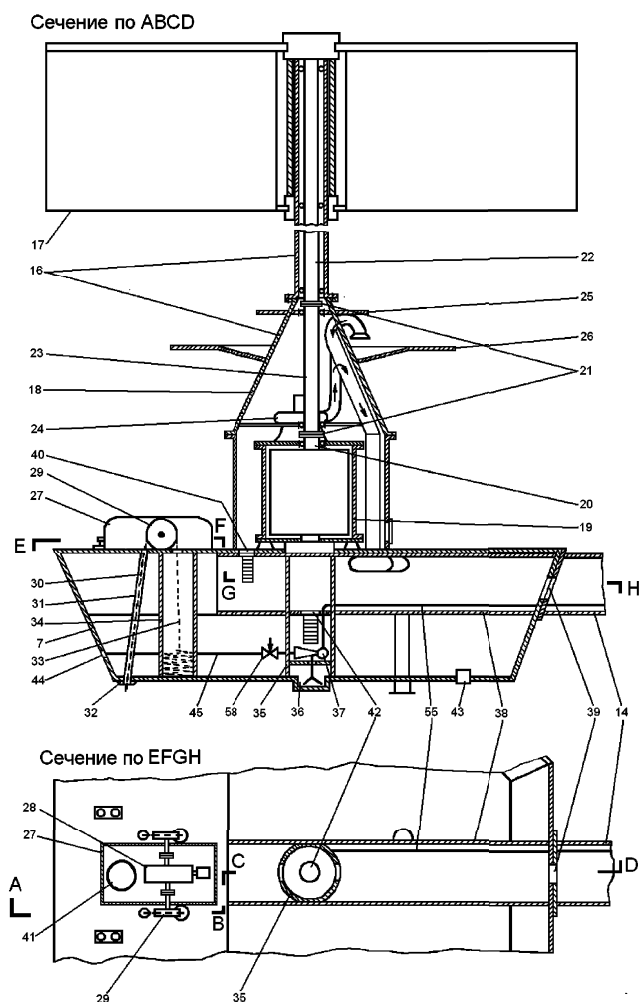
Конструкция одного из угловых поплавков в сборе с ветрустановкой
